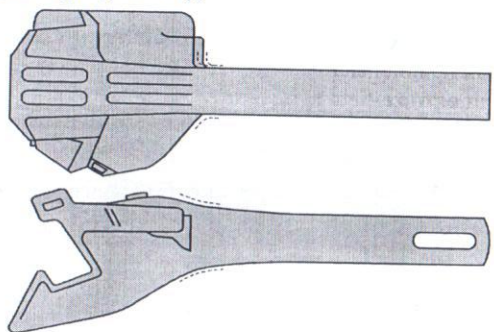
Контроль переходов от хвостовика к головной части корпуса автосцепки
